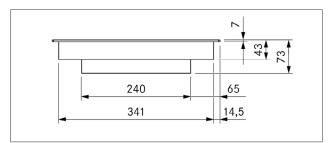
Dimensões do aparelho PKCH3, vista dianteira
